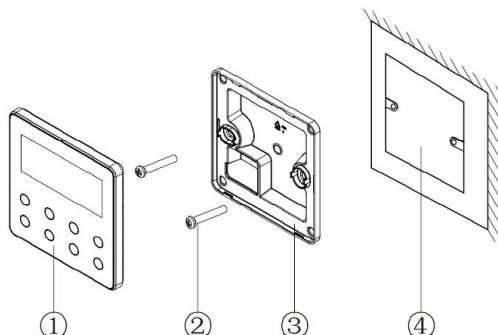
Instrukcja montażu sterownika przewodowego
